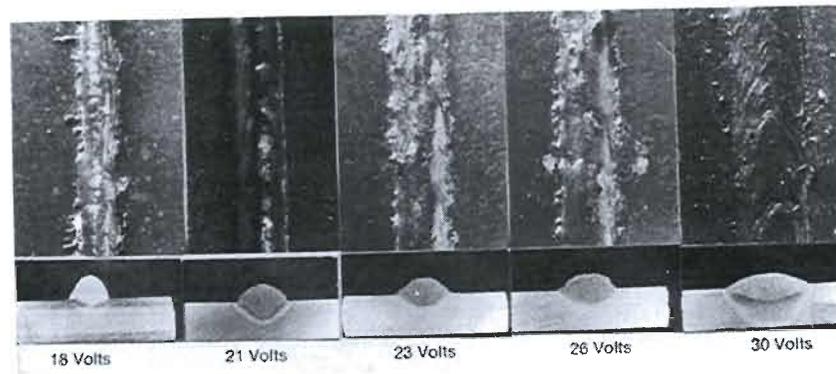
Efecto del voltaje del arco en el cordón y formación del mismo, condiciones de soldadura: corriente 175 amp velocidad 15"/min, tamaño del electrodo 0.035" gas CO₂ stick out de 3/8"
